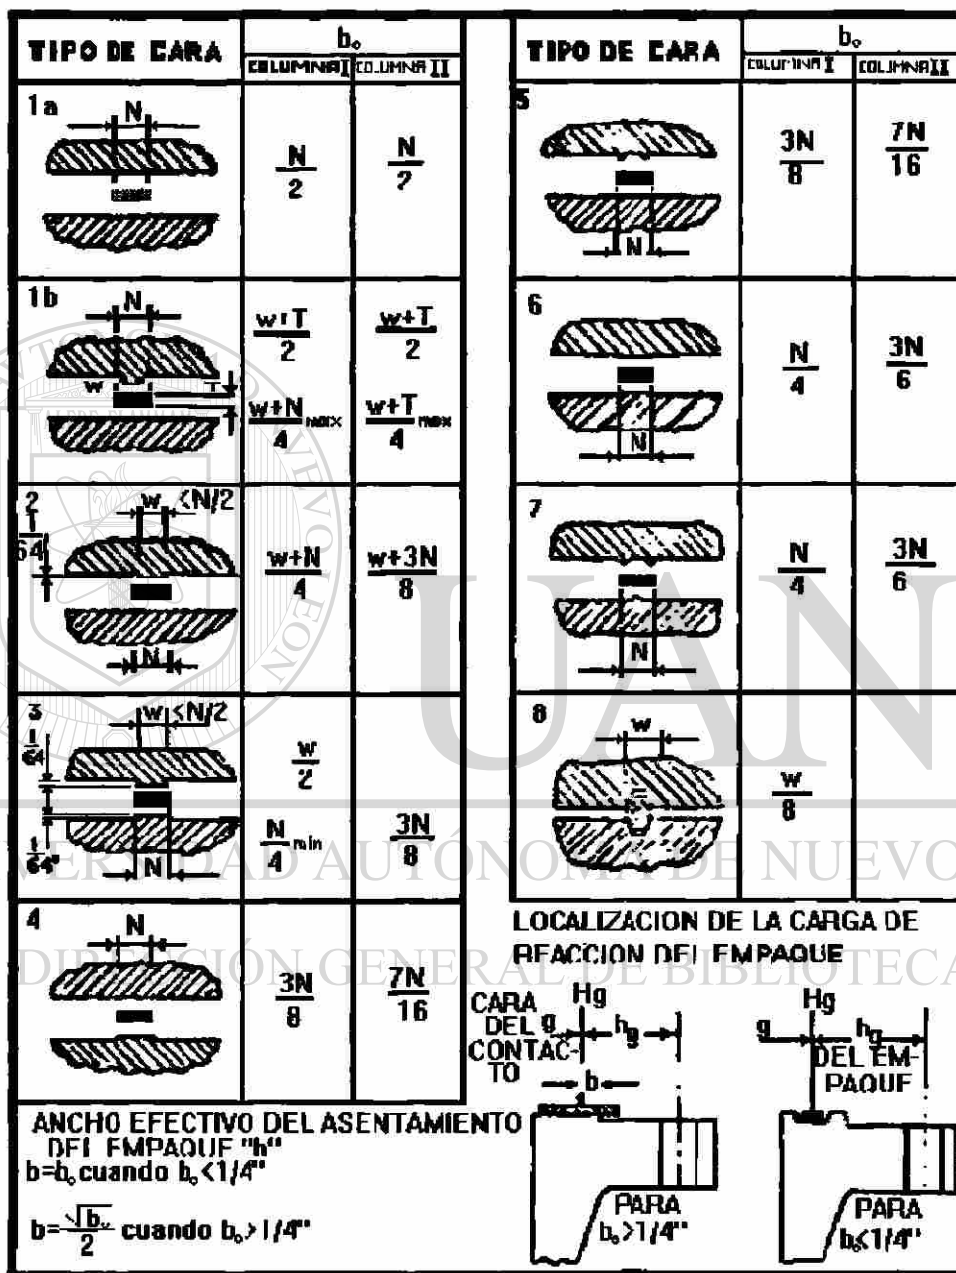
Ancho efectivo del asentamiento del empaque, b.
